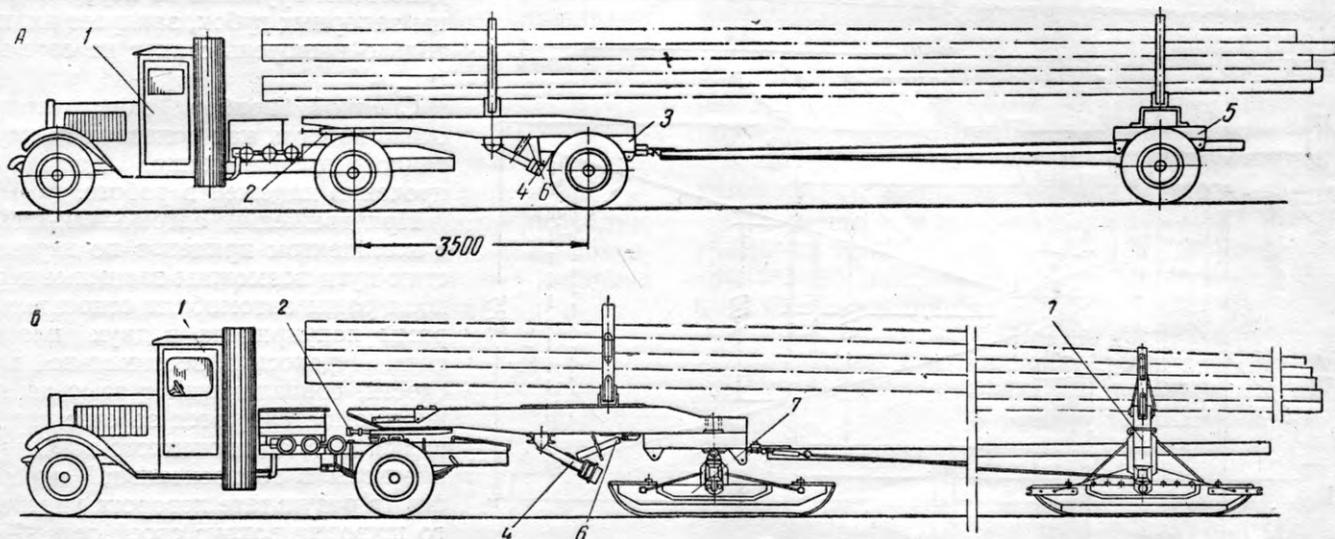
Общий вид автопоезда с колесными (А) и санными (Б) прицепами:
